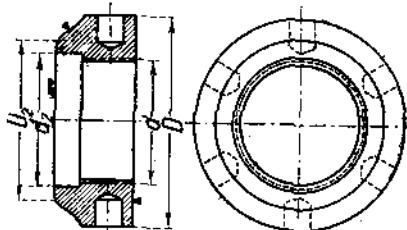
Гайка отжимная цилиндрическая для упорных центров с мелкой метрической резьбой.
